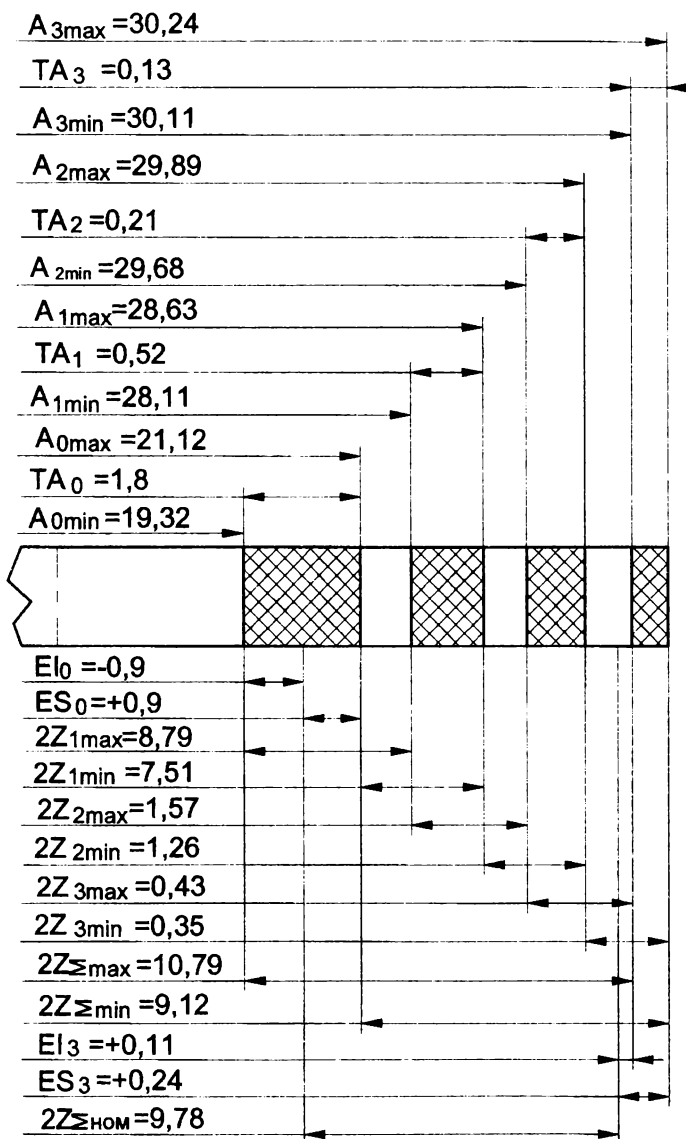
Схема расположения припусков, допусков и предельных размеров для отверстий диаметром $30^{+0,24}_{+0,11}$
